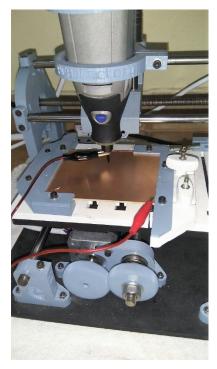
Router CNC Cyclone PCB Factory. Fonte: Imagem do autor
